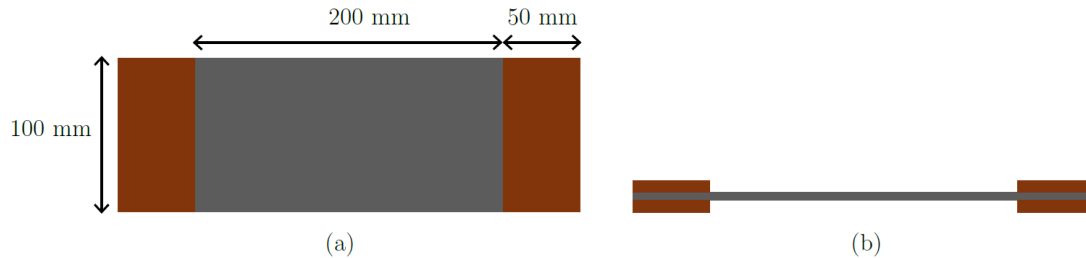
Eprouvette utilisée pour l'étude - (a) Vue de dessus (b) Vue de profil
